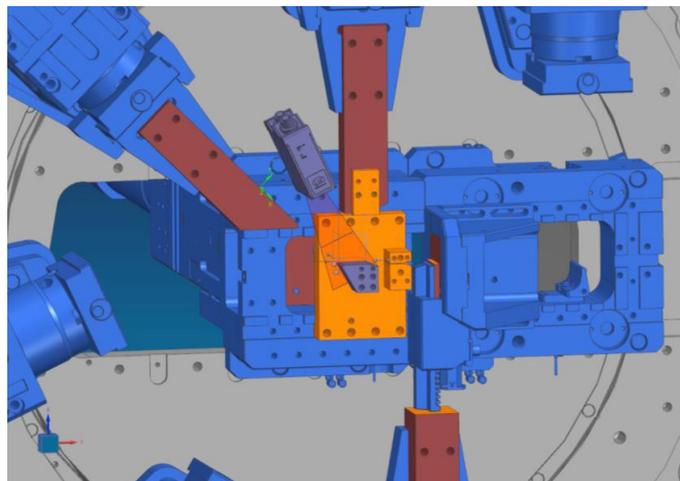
CAD-Darstellung des geplanten Werkzeugs.
